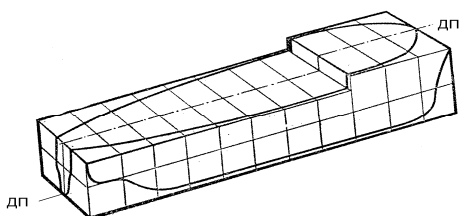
Розмітка бруса для виготовлення корпусу моделі з цілого шматка деревини
